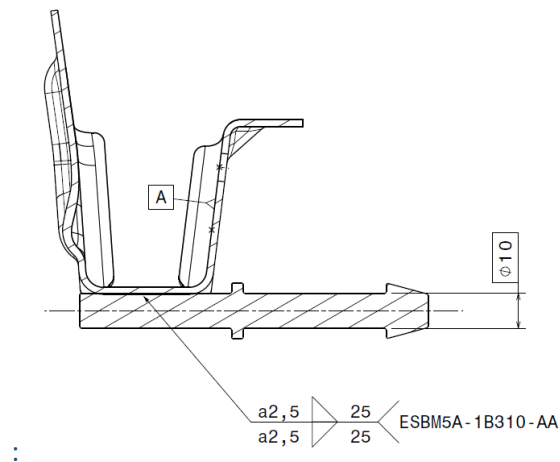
Corte transversal por el eje de simetría de la pieza. Imagen extraída del plano.
